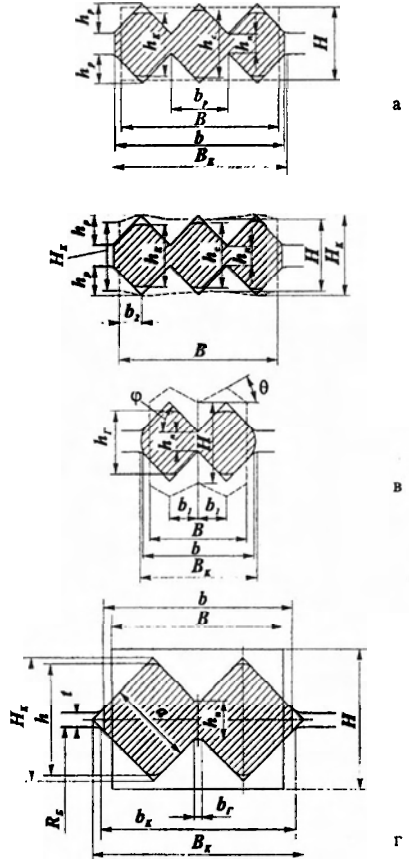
Схемы деформации металла на трехручьевых калибрах при прокатке плоской (а) и профильной (б) заготовок, и в двухручьевых калибрах с ромбической (в) и квадратной (г) формой ручьев.
